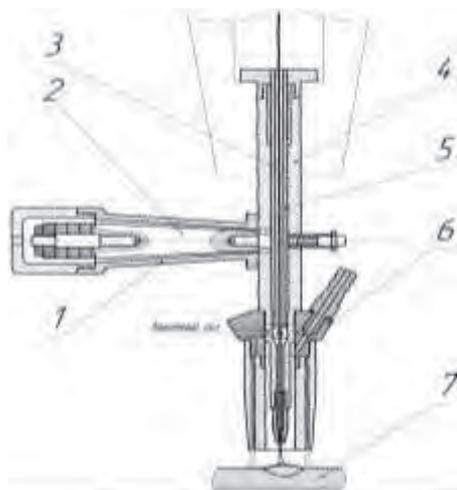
Схема технологической оснастки для наплавки с ультразвуком и металлопорошковой присадкой: 1 – устройство передачи УЗК на электрод; 2 – волновод-концентратор; 3 – электродная проволока; 4 – корпус наплавочной головки; 5 – токовод; 6 – устройство для подачи газопорошковой смеси; 7 – наплавляемая поверхность
